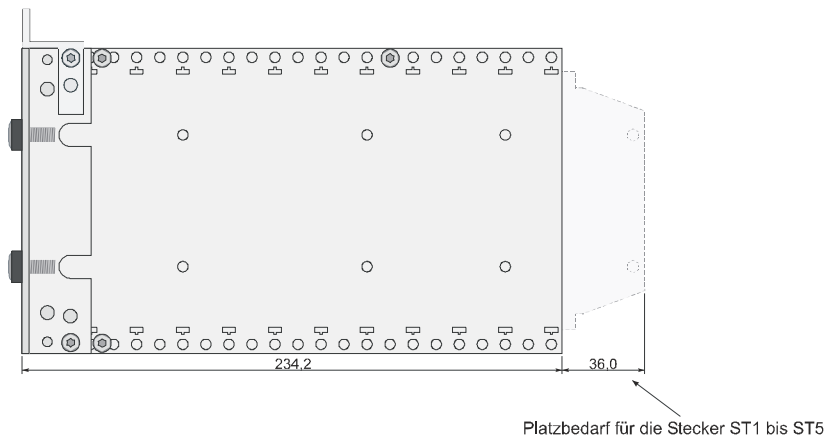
Seitenansicht des Baugruppenträgers Type BGT05 mit Beschriftungsleiste (identisch mit BGT04)
